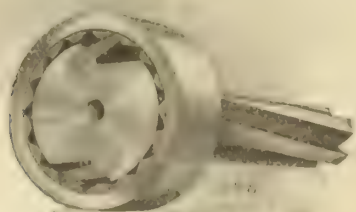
Umsetzvorrichtung der Ingersoll-Maschine
